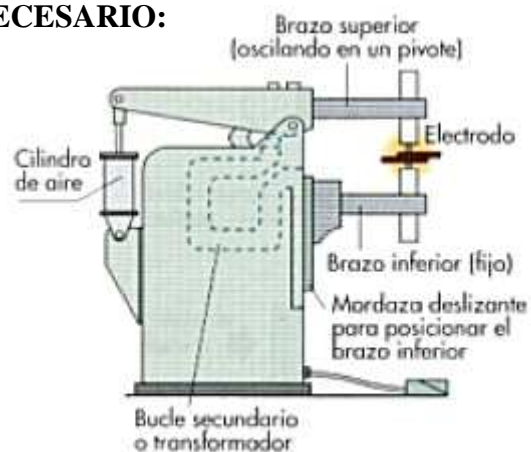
Equipo necesario para la soldadura a tope
